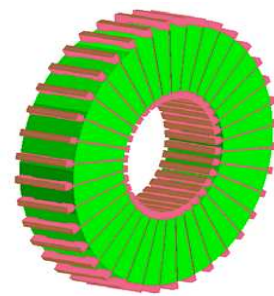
Bobinage Gramme pour machine à flux axial [QU 03]
